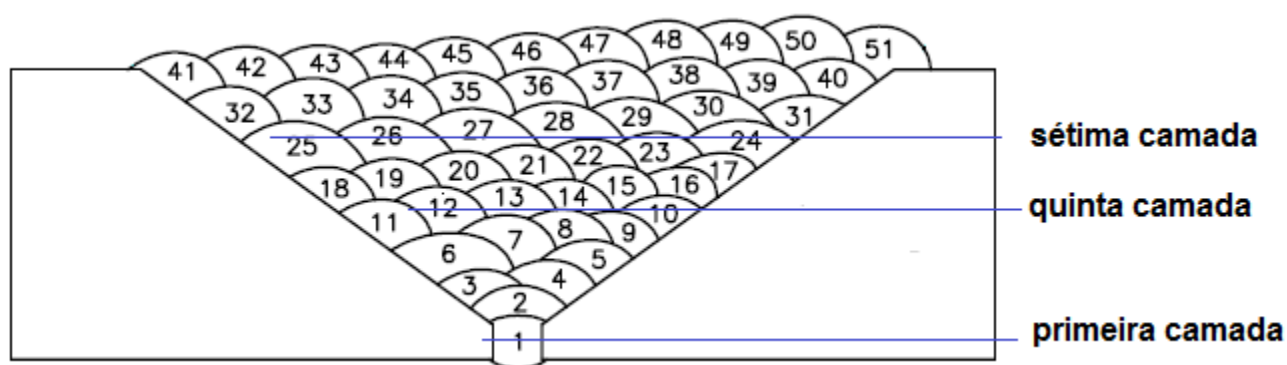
Sequência da soldagem e distribuição das camadas de solda.
